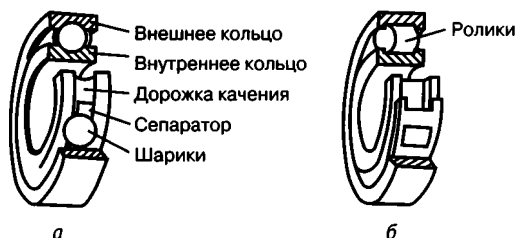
Устройство шарикового (а) и роликового (б) подшипников качения
